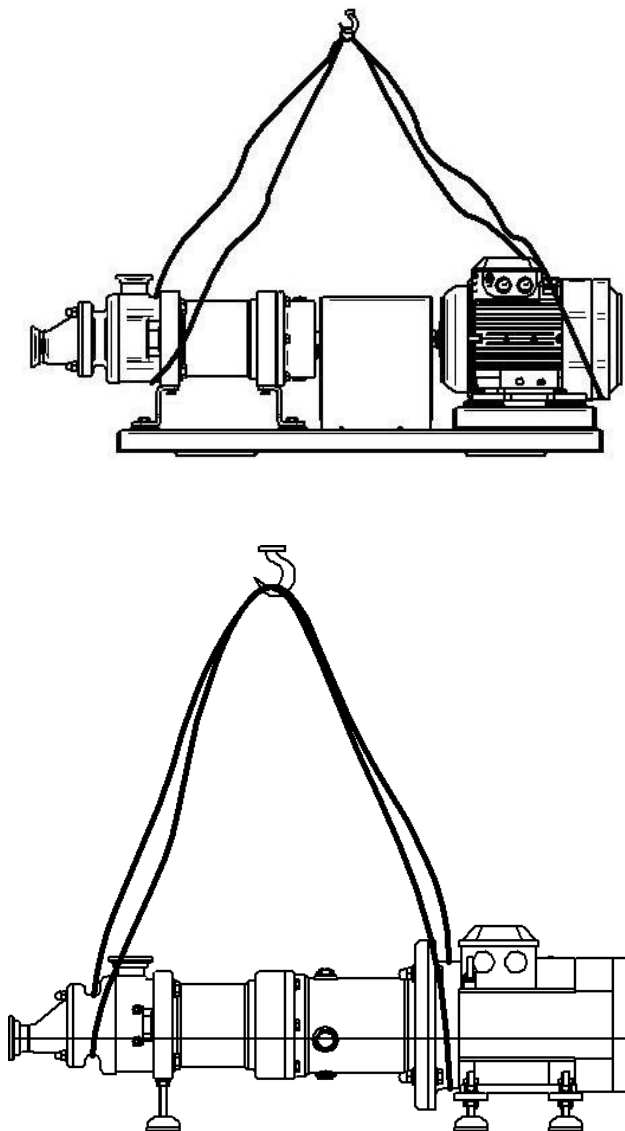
Крепление подъемных тросов насоса к опорной плите.
